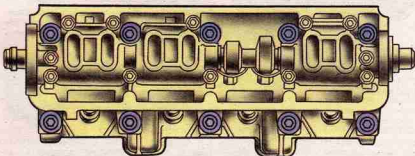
Порядок затягивания болтов головки цилиндров
